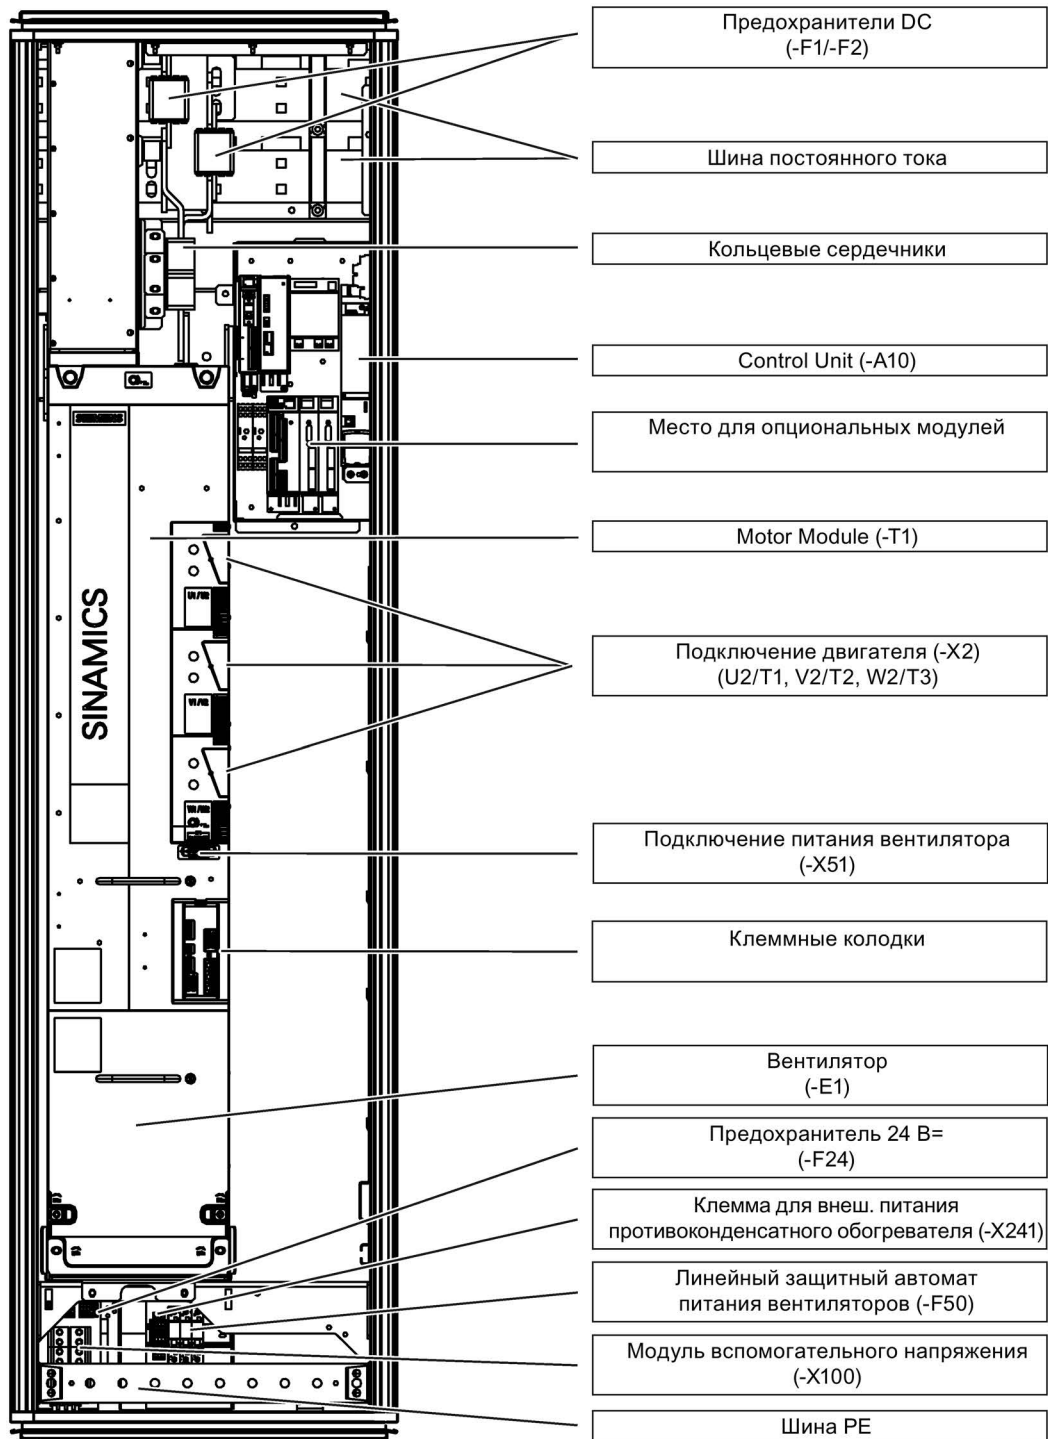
Пример сборки модуля двигателя – формат «шасси-2» (типоразмер FS4)
